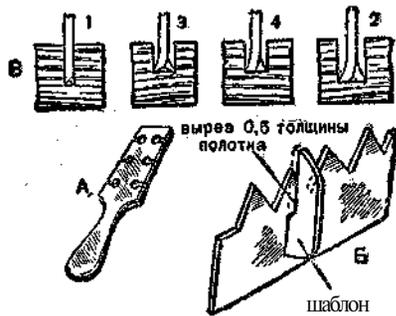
Разведение зубьев: А — разводка; Б — шаблон для проверки развода зубьев; В — профиль разведенных зубьев; 1 и 2 — неправильно, 3 и 4 — правильно.
